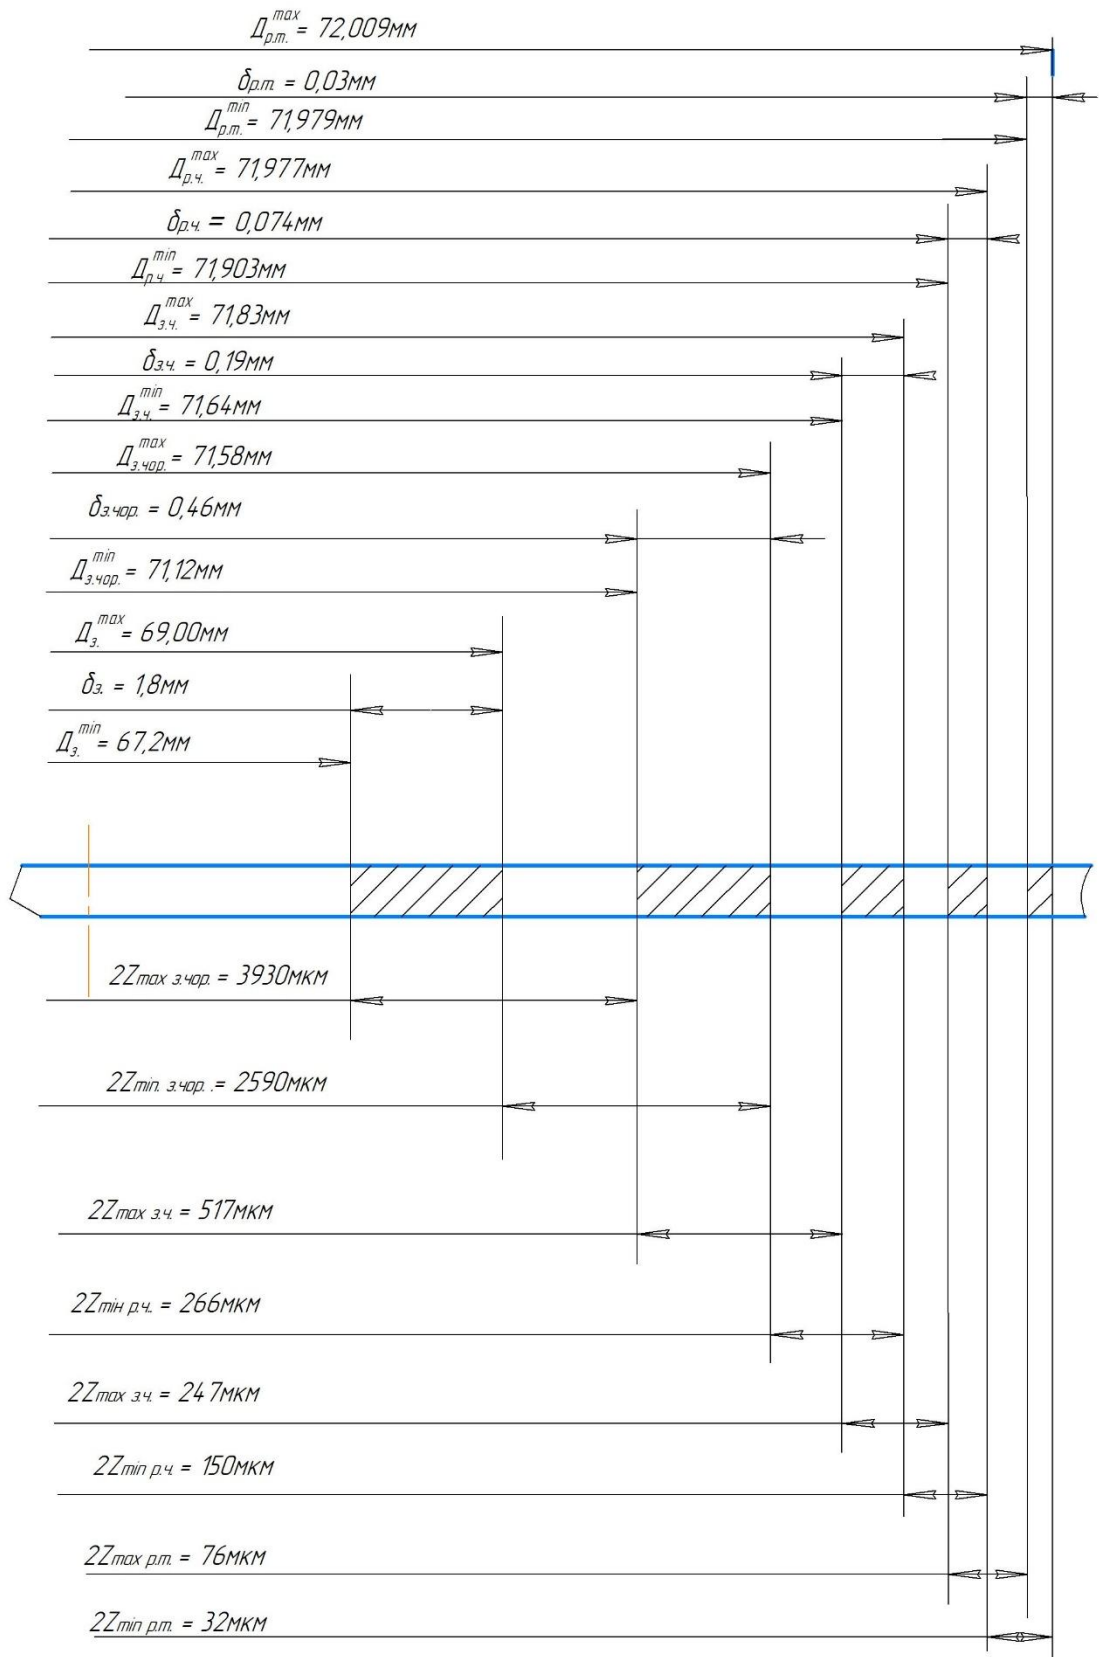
Схема розташування припусків для поверхні Ø72K7
